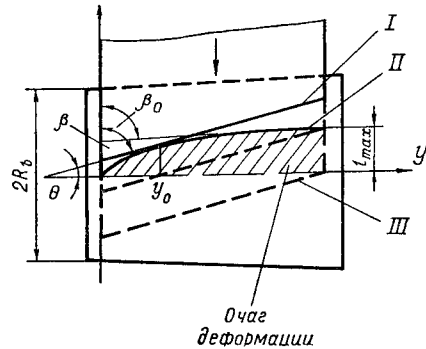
Схема подачи заготовки в очаг деформации при обрезке полосы под углом β :
